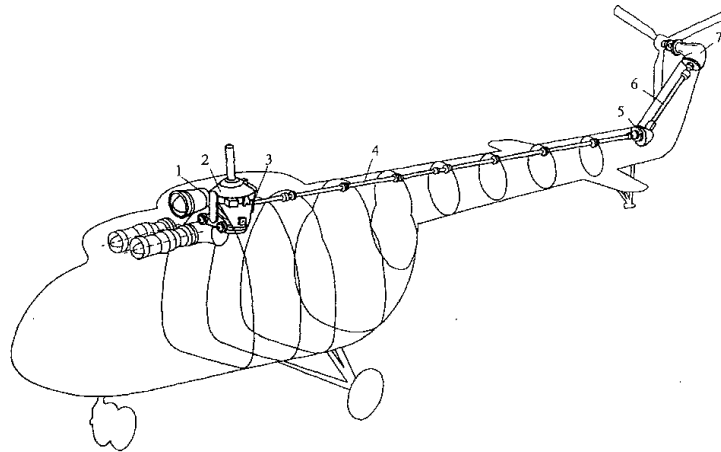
Компоновка трансмиссии вертолета: 1 промежуточные редукторы 2 главный редуктор, 3 тормоз несущих винтов, 4 вал рулевого винта, 5 промежуточный редуктор, 6 промежуточный вал, 7 редуктор рулевого винта.
